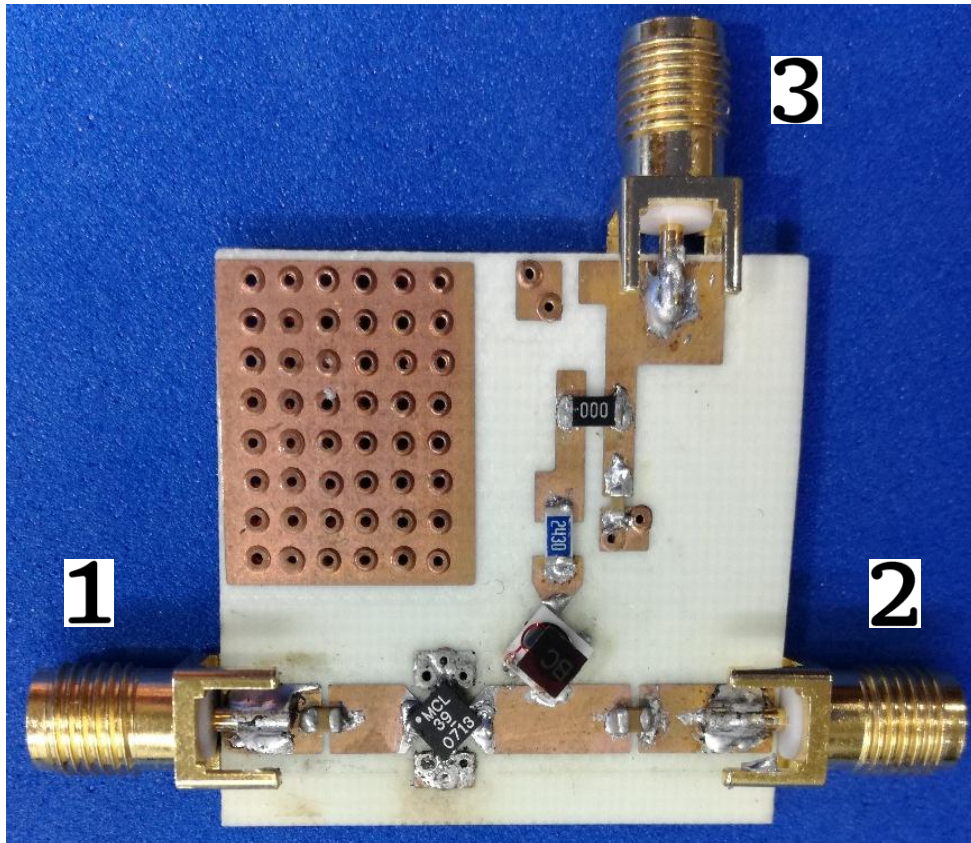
PCB fabricada a partir del diseño propuesto para el LEE-39+.
